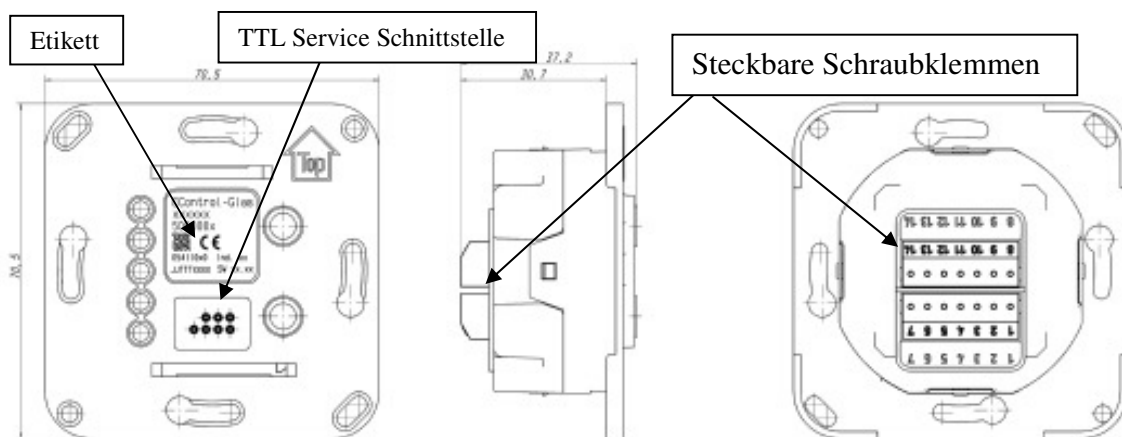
Front-, Seiten- und Rückansicht des Steuergerätes (STE, BDE) ohne Frontdeckplatte
